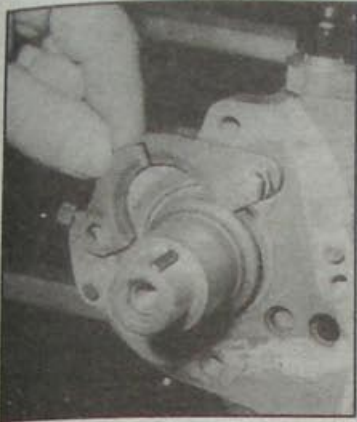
Снятие стопорной пластины фиксации крышки промежуточного вала на двигателе F3R 728
